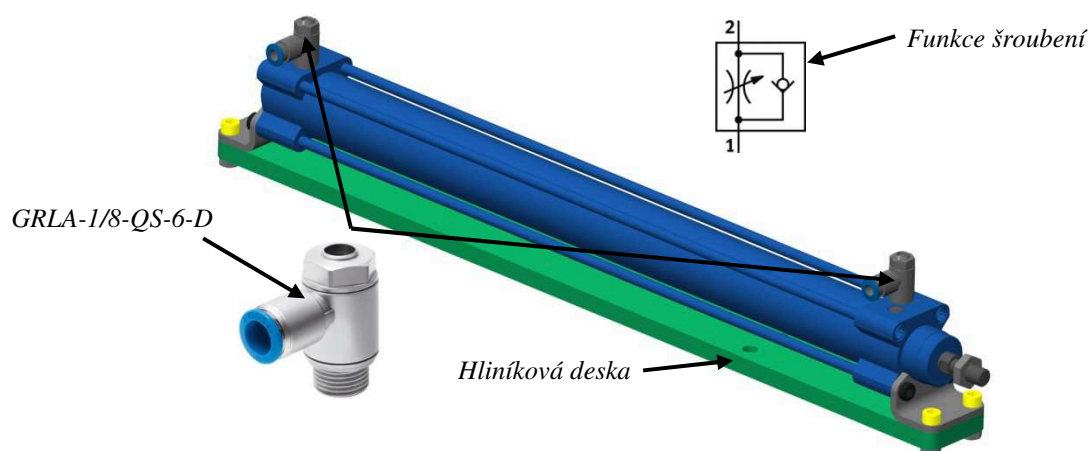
Pneumatický válec ADN-32-75-I-P-A pro vyrážení držáku ZHB
